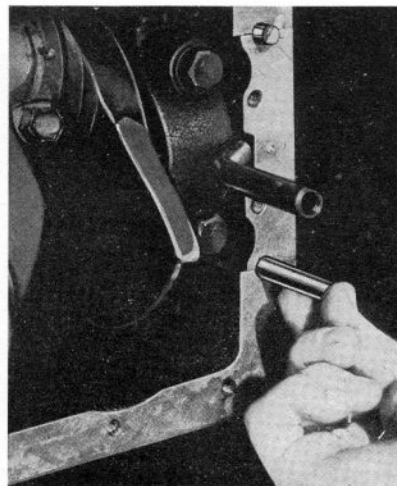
Joints du chapeau de palier arrière du vilebrequin.
